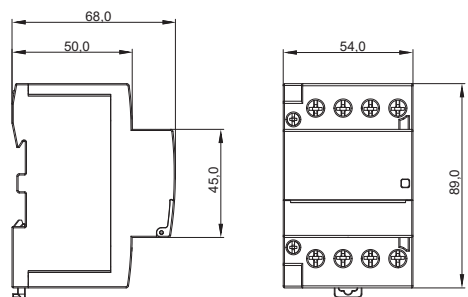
Габаритные размеры контакторов от 40 А до 63 А / Figure 4 – Overall dimensions of contactors from 40 A to 63 A
